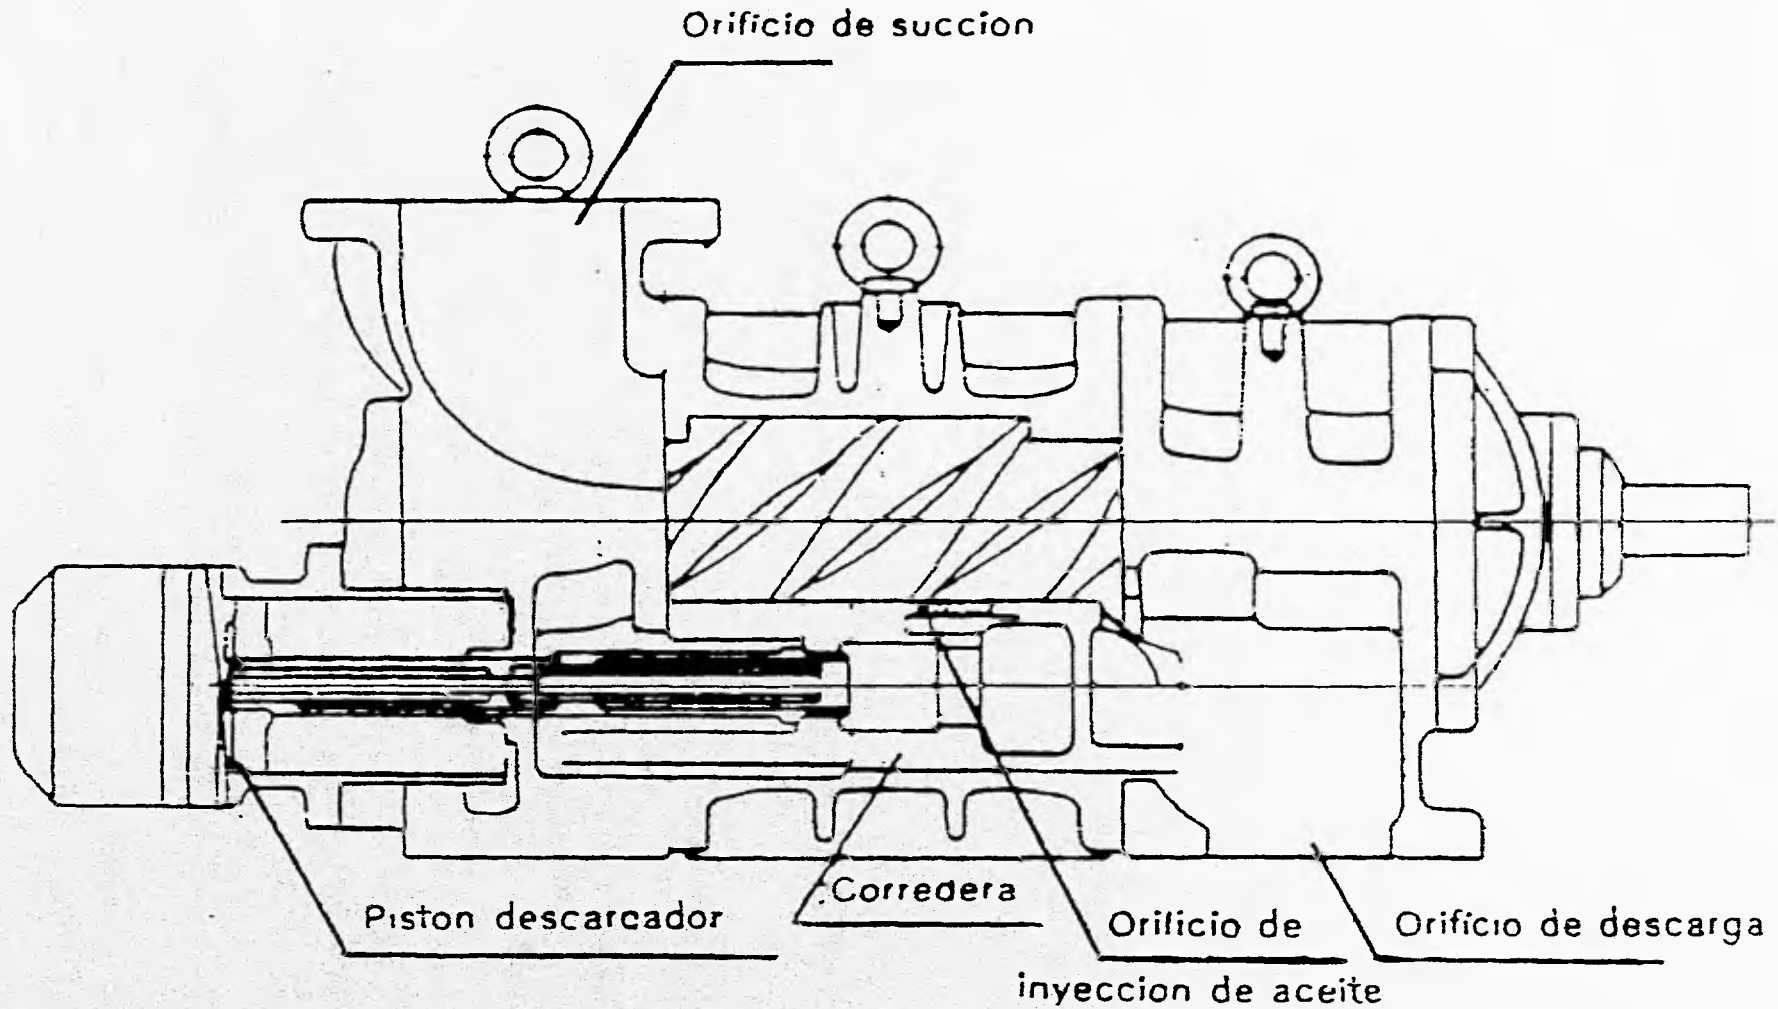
VISTA LATERAL DE CORTE TRANSVERSAL DE UN COMPRESOR TORNILLO.
